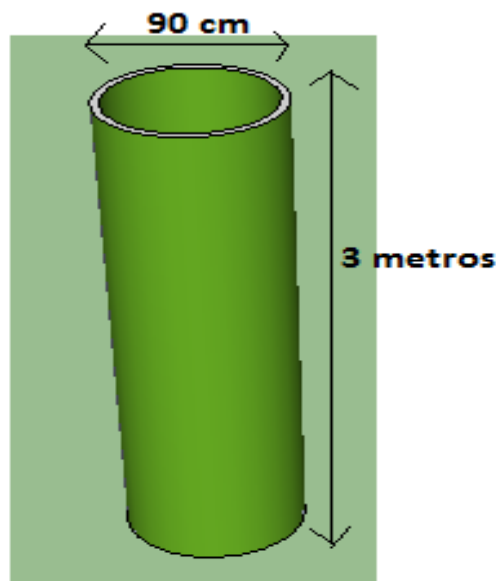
Dimensiones de un ventilador de la máquina de espumado.
